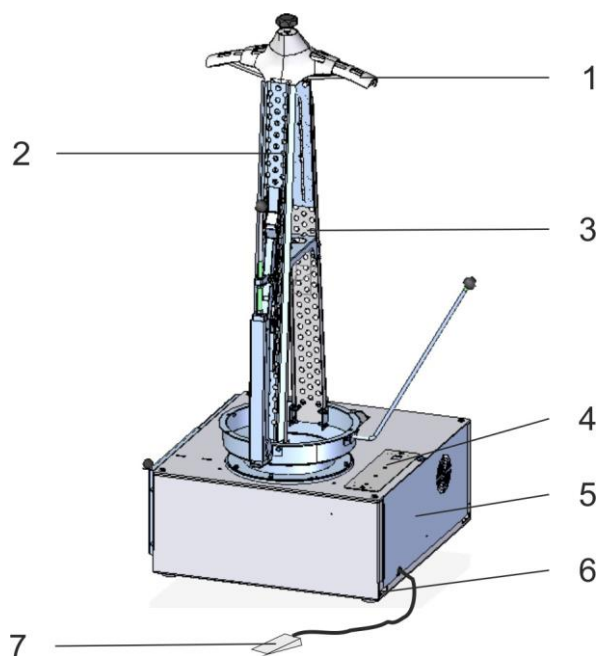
Visão geral da máquina, acabador universal com acessório de roupa - UF30 U
